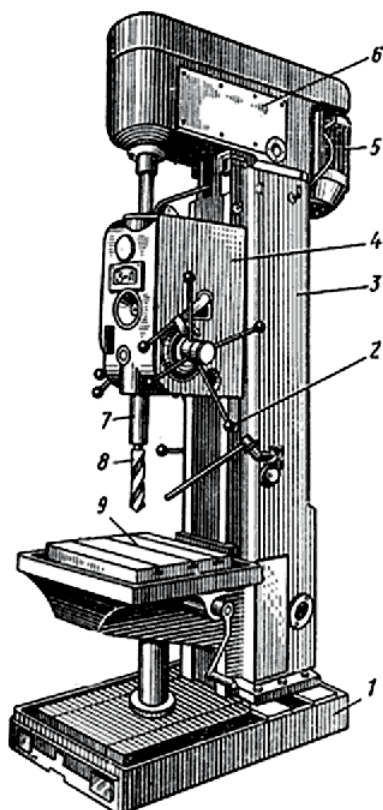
Одношпиндельный вертикально-сверлильный станок
